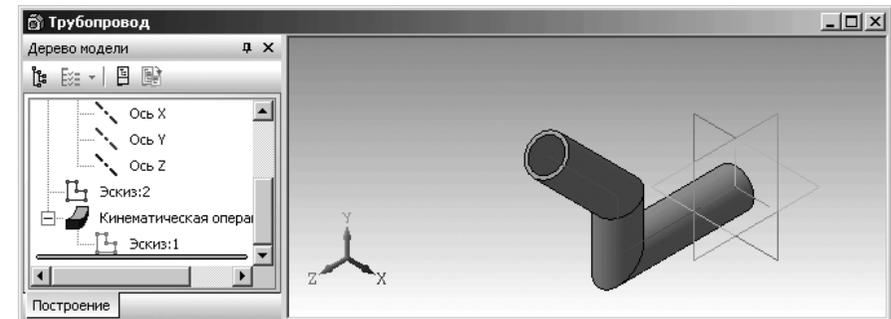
Модель трубопровода с установленной толщиной стенки
